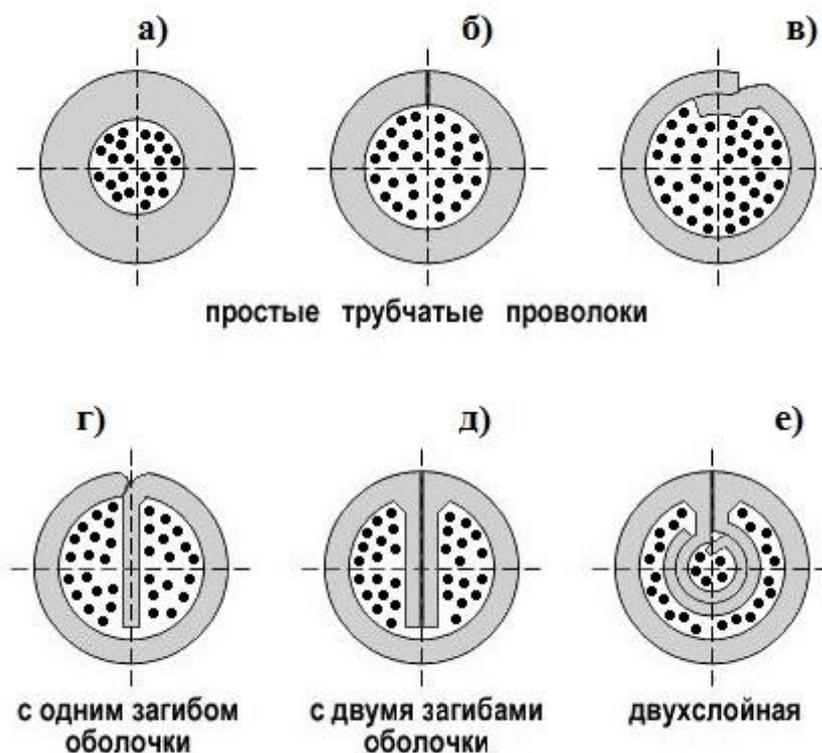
Виды порошковой проволоки по форме сердечника
